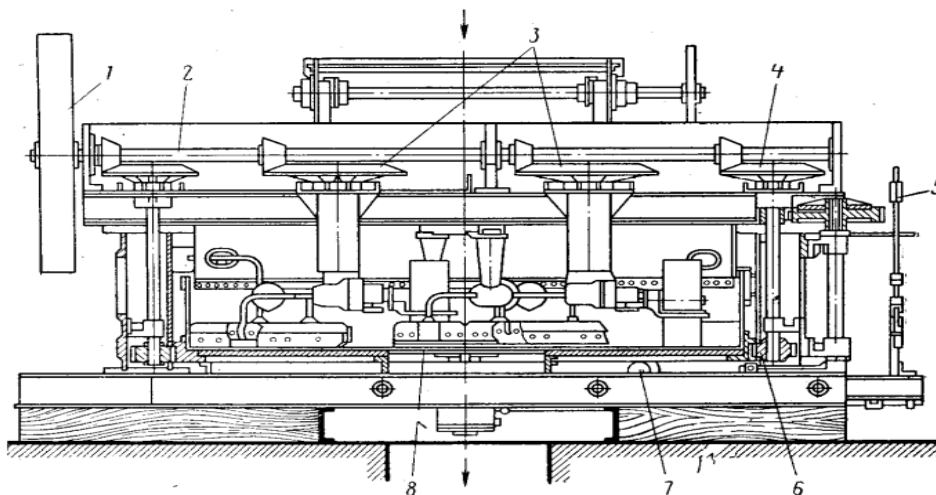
Схема двухроторного бігунково лопатевого змішувача
